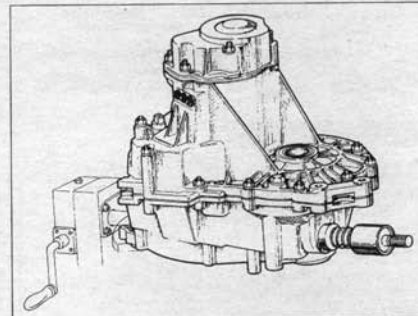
Коробка передач, установленная на стенде для разборочно-сборочных работ
